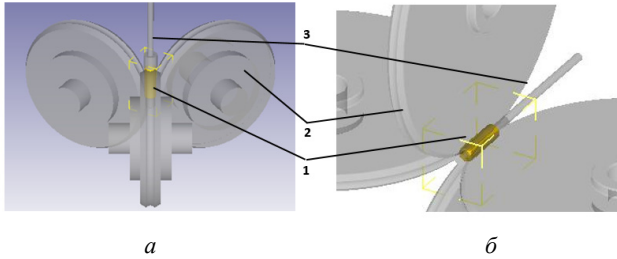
Схема обтиску трубчастої заготовки (профільна оправка не показана) ротаційним куванням (1 – трубчаста заготовка; 2 – ролики; 3 – бійки радіальної дії)
